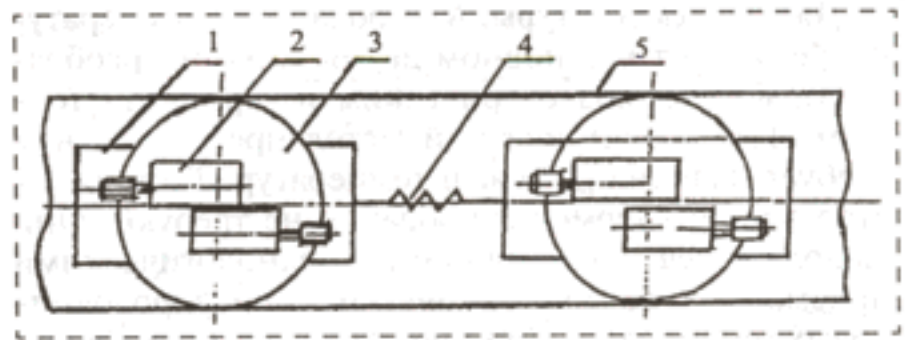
Схема мобильного робота для движения в трубе: 1 — платформа; 2 — электродвигатель; 3 — колесо-редуктор; 4 — гибкая сцепка; 5 — труба
